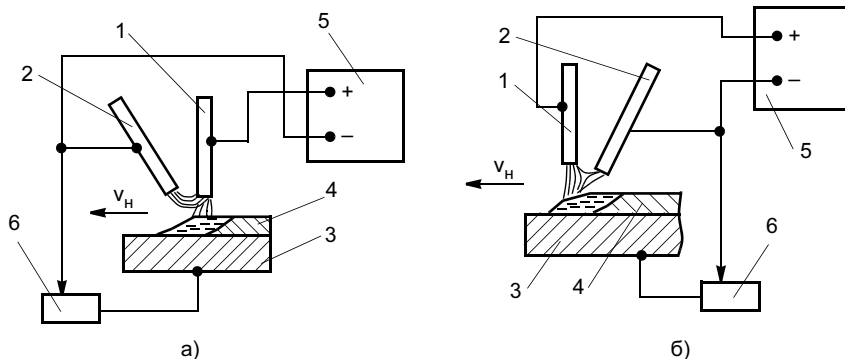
Схема двухэлектродной наплавки проволоками под флюсом с одной заземленной проволокой ( $v_n$  — скорость наплавки): 1 — основная проволока; 2 — дополнительная заземленная проволока; 3 — основной металл; 4 — наплавленный металл; 5 — источник питания; 6 — балластный реостат
